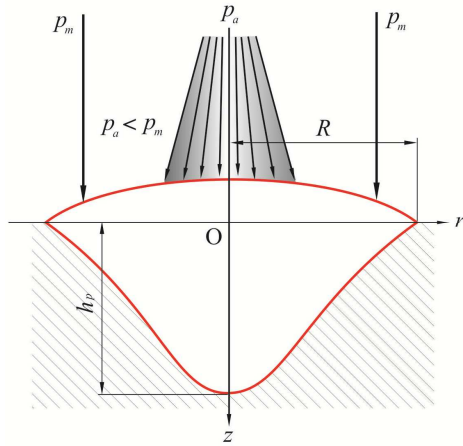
Схема баланса давлений в сварочной ванне при неподвижном источнике нагрева
